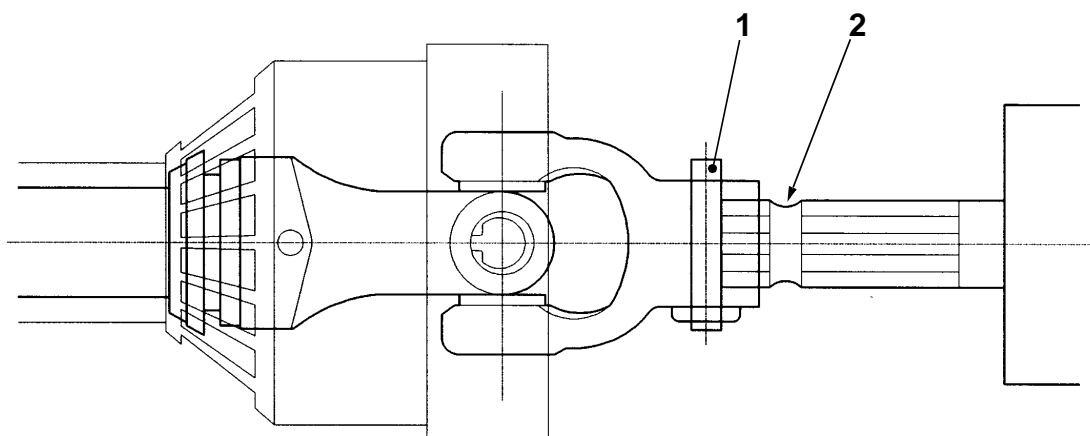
Collegamento albero cardanico con spina di sicurezza
